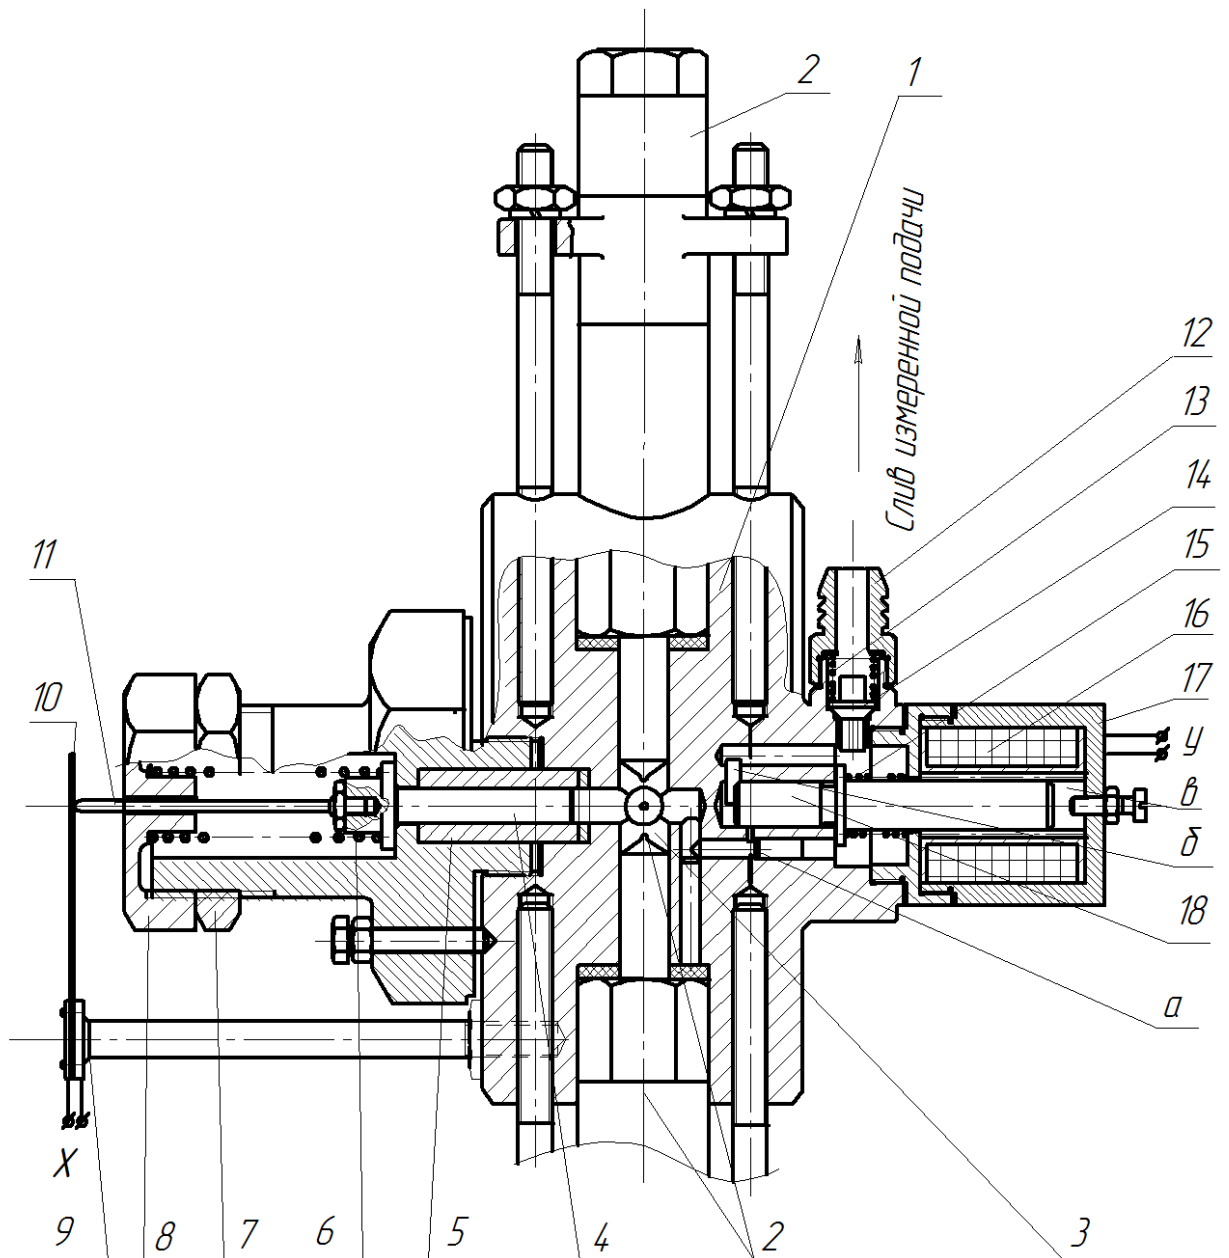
Устройство для измерения величины, неравномерности и закона подачи топлива: 1- корпус; 2- форсунки; 3- камера измерительная; 4- плунжер; 5- втулка плунжера; 6-пружина; 7- контргайки; 8- гайка регулировочная; 9- датчик хода измерительного плунжера; 10- пластина измерительного плунжера; 11- шток; 12- штуцер; 13- пружина; 14- клапан перепускной (грибкового типа); 15- пружина электромагнитного клапана, 16- катушка электромагнитного клапана; 17- корпус электромагнитного клапана; 18- плунжер электромагнитного клапана
